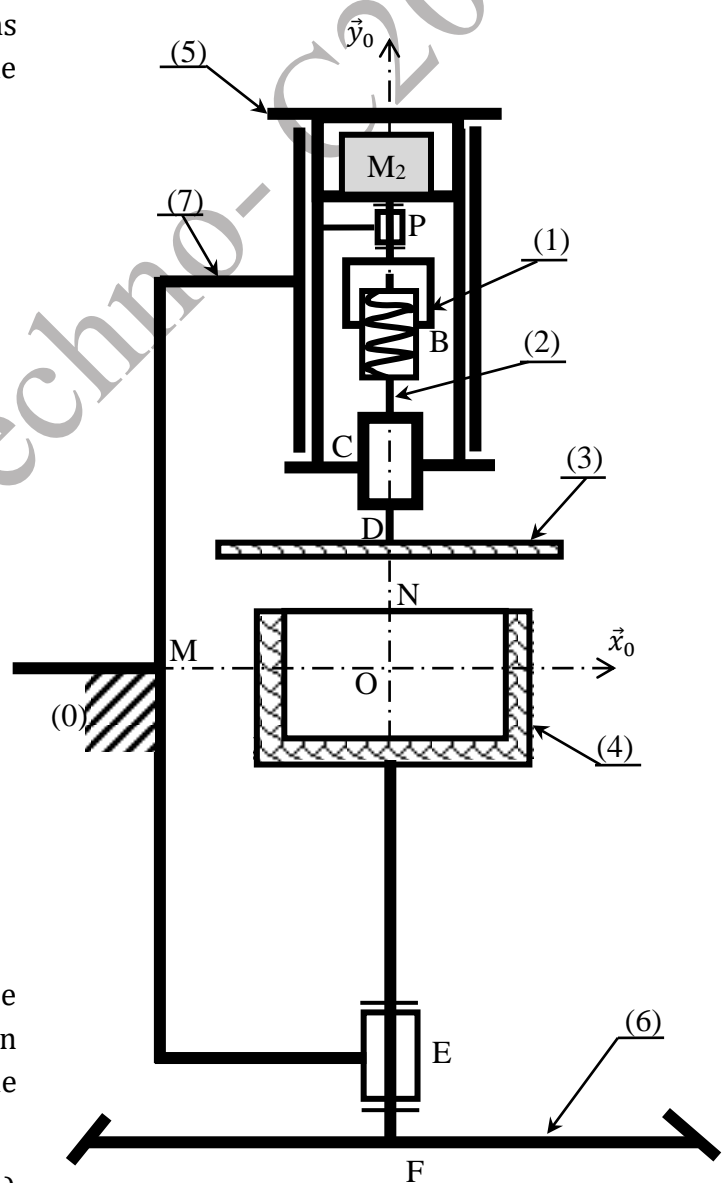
Unité de fermeture et d'ouverture du moule (moule (4) ouvert)
